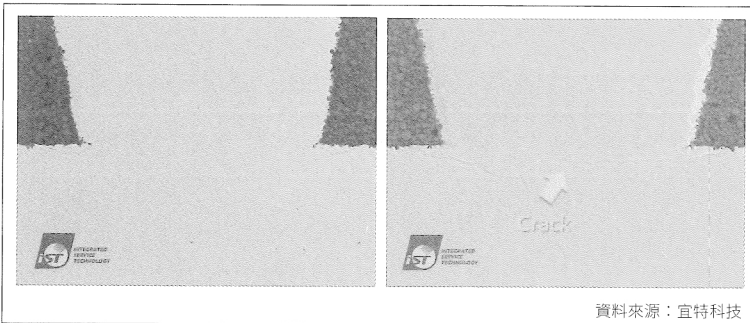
(左), 為傳統機械研磨後之PCB via, 無法看到Crack ; (右)為CP milling後之PCB via, 清楚呈現Crack
